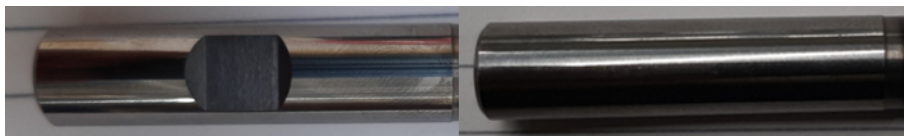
Haste da ferramenta (à esquerda - *Weldon*, à direita - cilíndrica), cortesia: *Palbit
